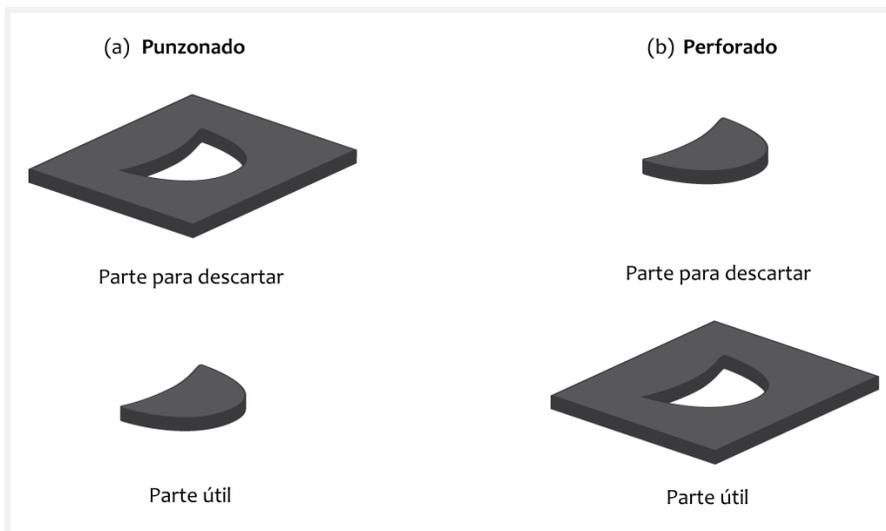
(a) Operación de punzonado (b) Operación de troquelado.
